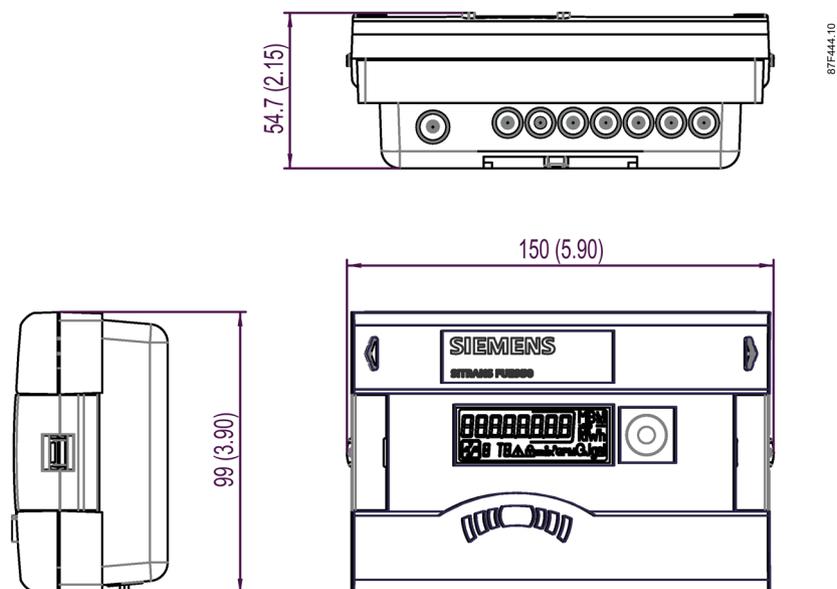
FUE950, dimensiones en mm (pulgadas)
